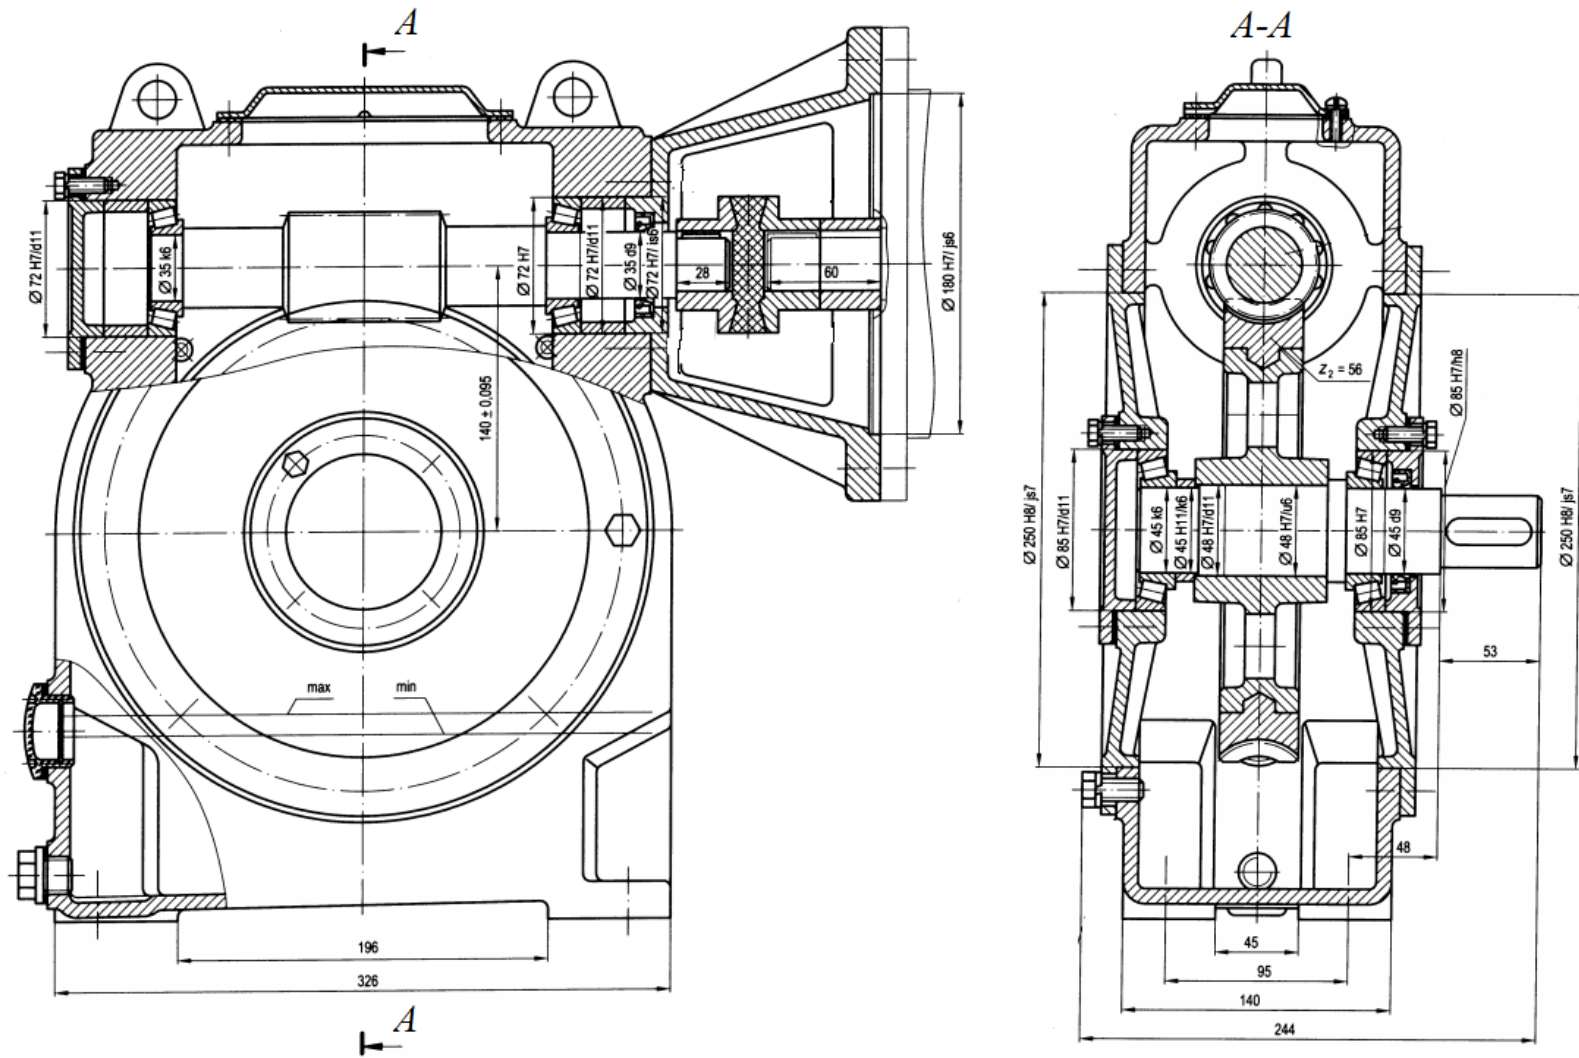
Конструкция червячного редуктора с верхним расположением червяка
